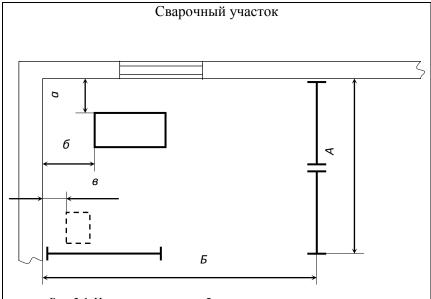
Нормы расстановки оборудования на сварочном участке
